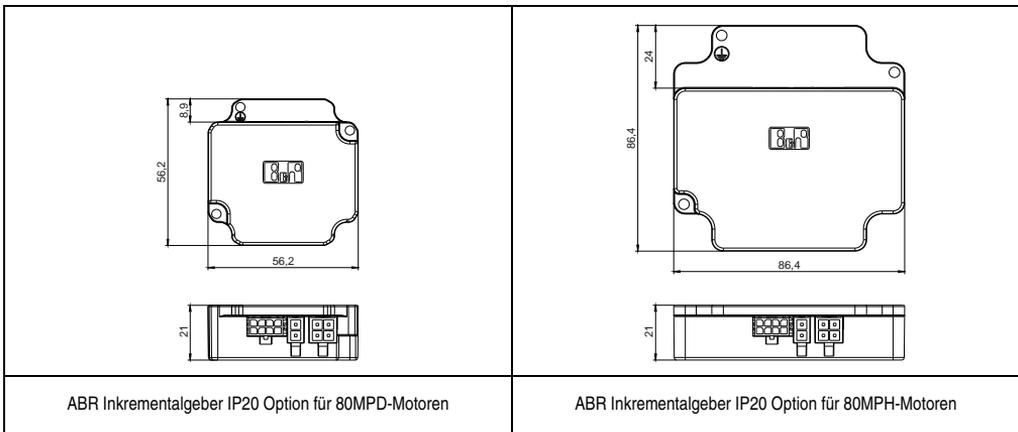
Schrittmotoren mit ABR Inkrementalgeber IP20 Option - Abmessungen
